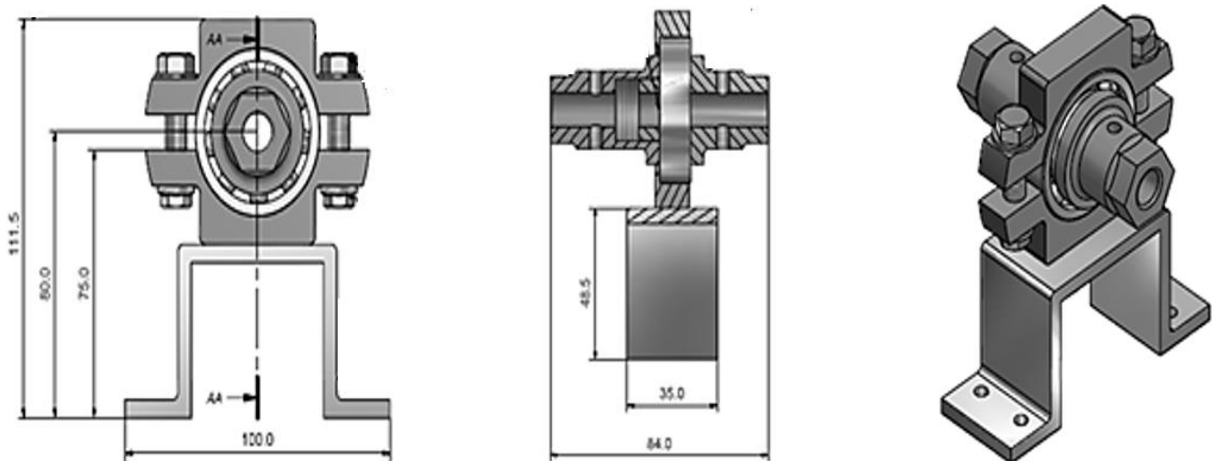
Ensamblaje del dispositivo mecánico para generar carga axial y radial en el banco diseñado
